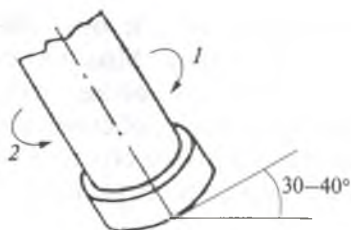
Положение трубы при сварке поворотных соединений внахлестку:
